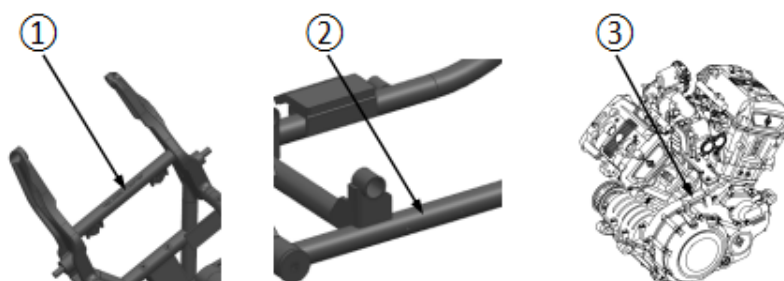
Схема расположения заводской таблички, номера рамы, VIN-кода и номера двигателя
